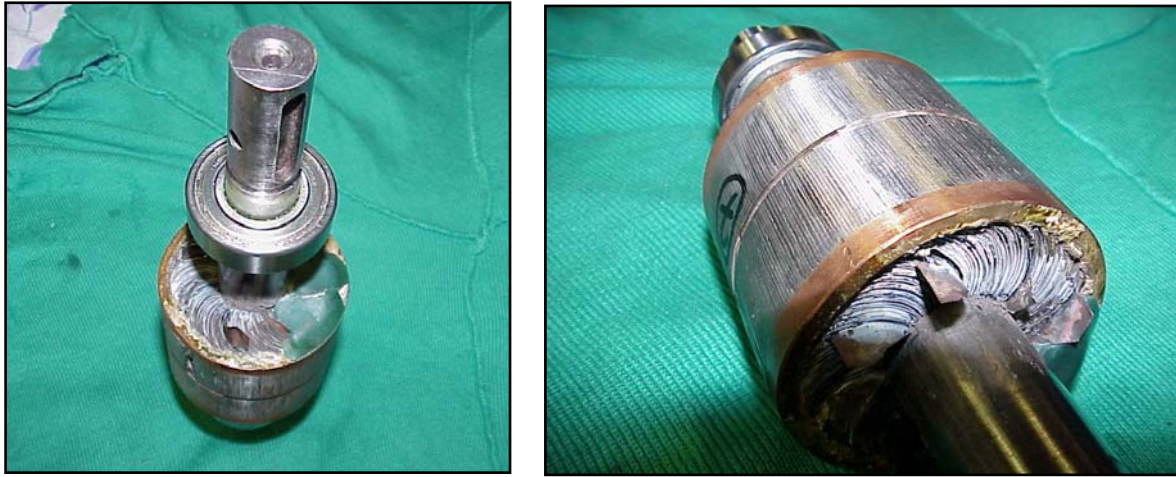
Detalles constructivos del rotor chapas tipo B. Obsérvense las chapas de ventilación.
